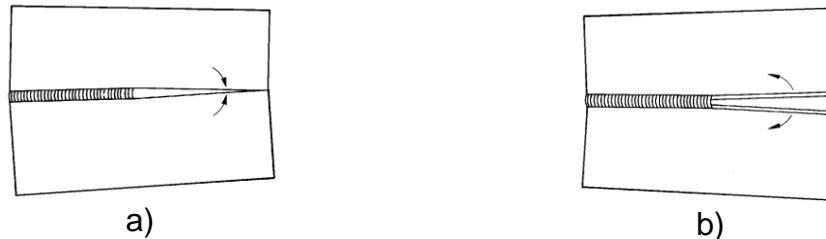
Rotación angular del metal frío frente al movimiento de la soldadura [51].
